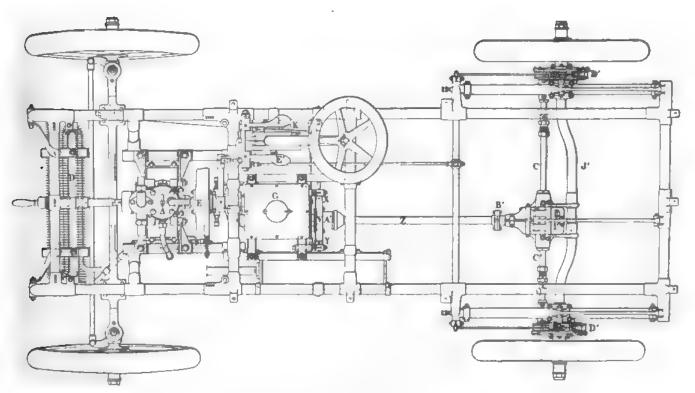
Grundriss des Hurtu-Wagens.
